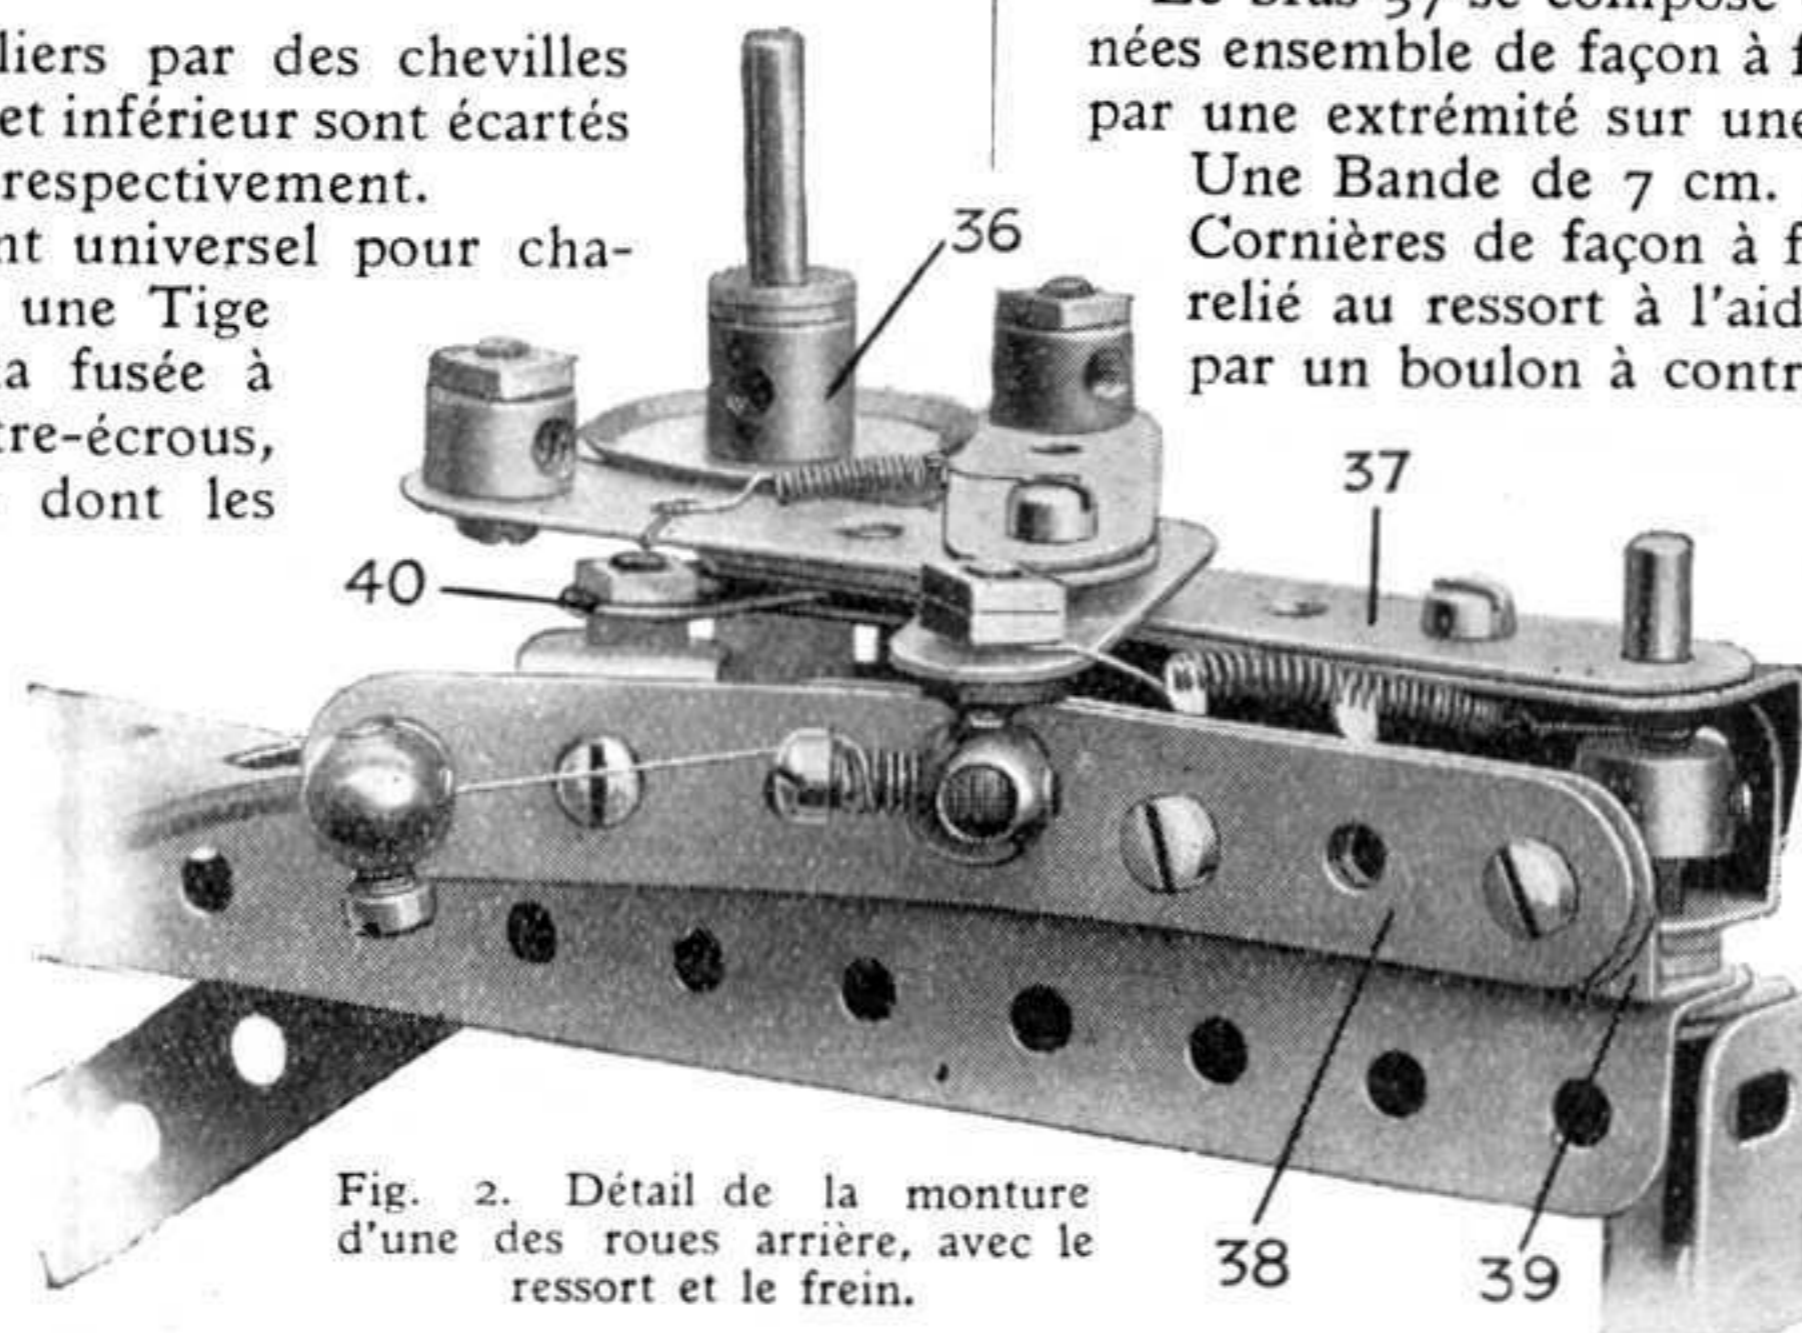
Détail de la monture d'une des roues arrière, avec le ressort et le frein.
